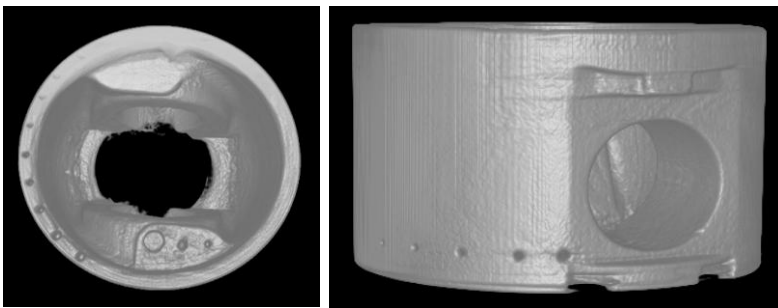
Слева показан торец поршня, а справа – фронтальный вид
